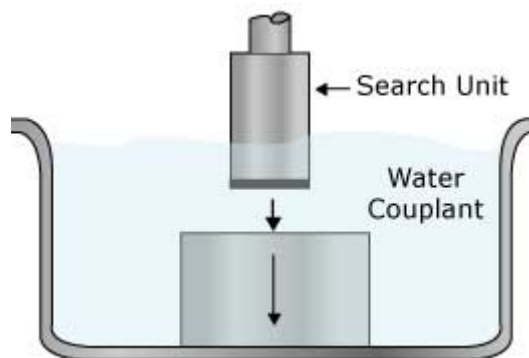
Técnica de inspección por inmersión utilizando agua como acoplante.
